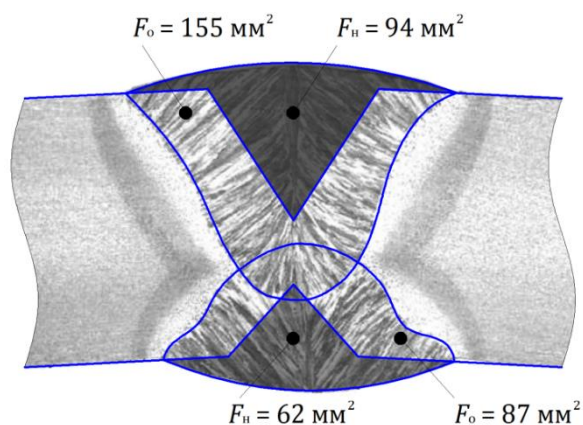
Макрошлиф сварного соединения:  $F_0$  – площадь поперечного сечения основного металла;  $F_n$  – площадь поперечного сечения наплавленного металла.
